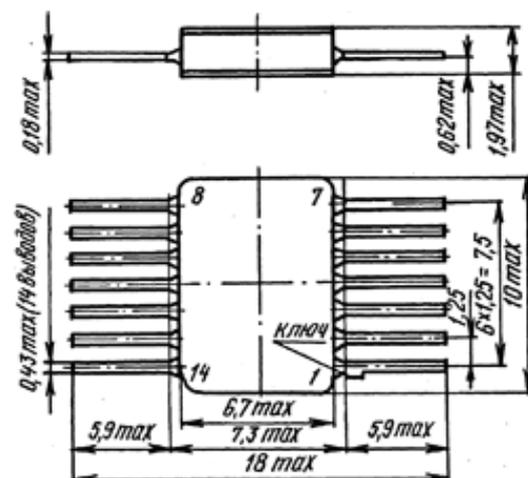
Габаритные чертежи корпусов 401.14-4 и 401.14-5M
